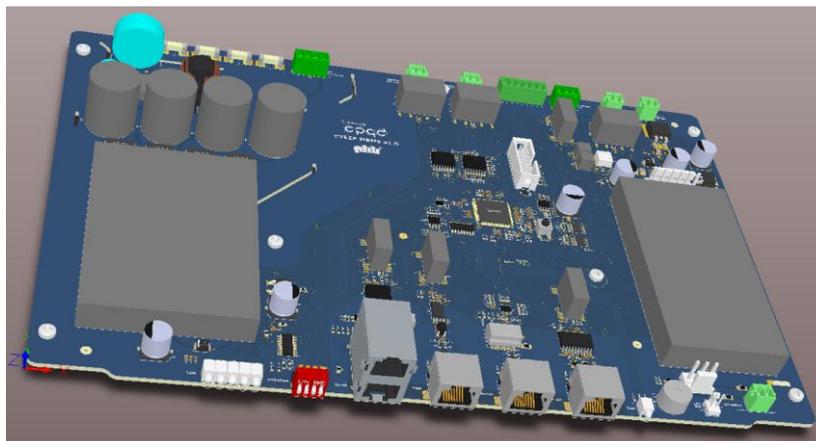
Ilustração da PCB do Módulo Mestre (MBMS)
